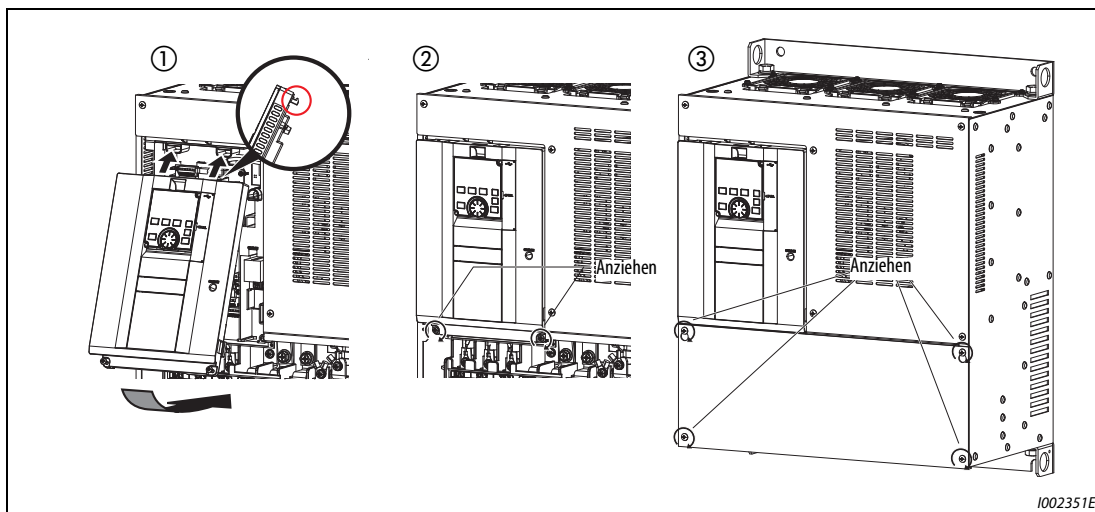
Anbringen der Frontabdeckung und der Klemmenblockabdeckung
